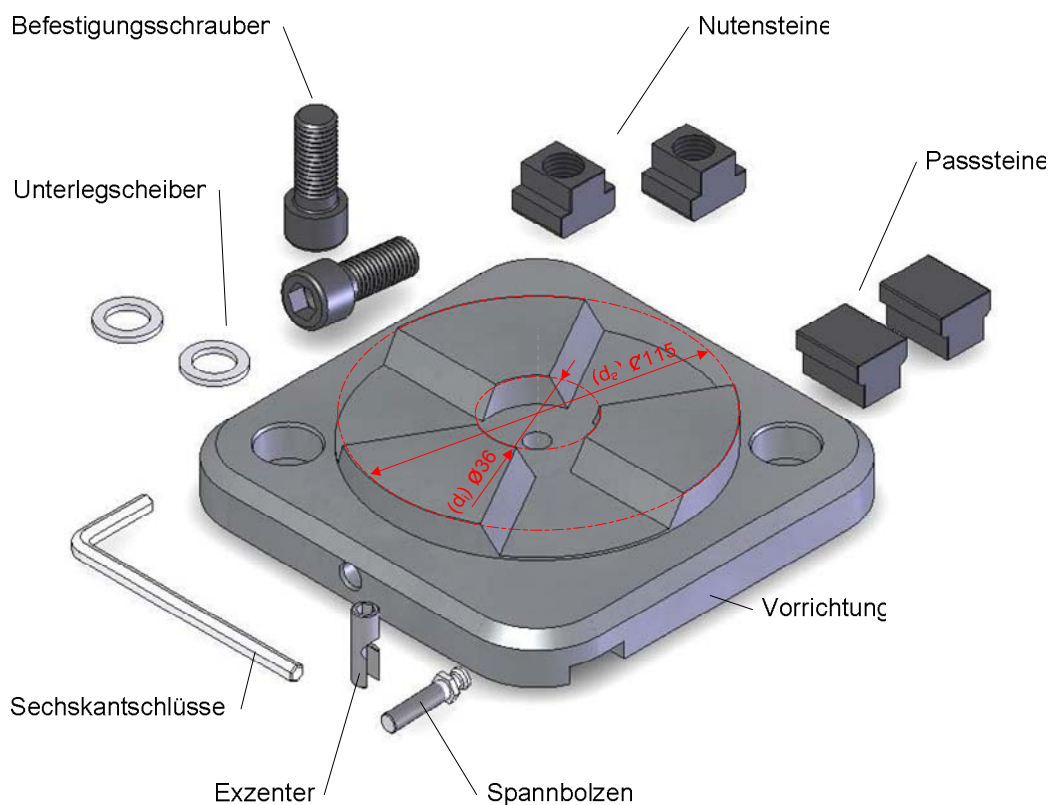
Vorrichtung mit Befestigungs- und Spannmittel für die Fräsbearbeitung
